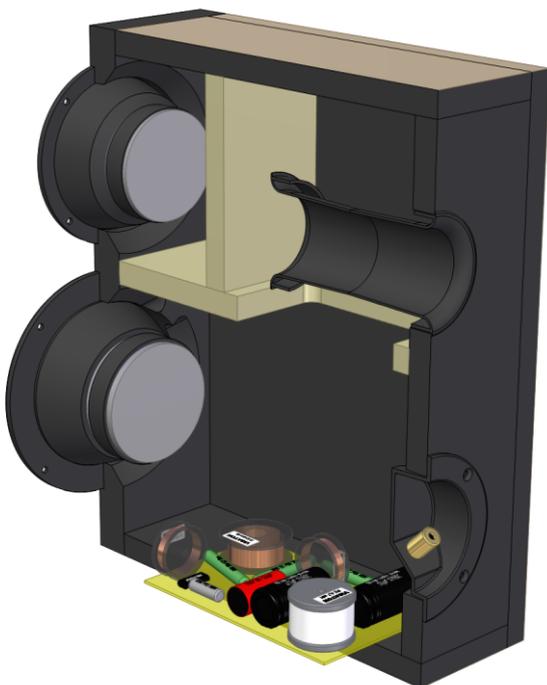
Schnittansicht zum Gehäuseaufbau und Innenansicht am Prototyp-Aufbau
